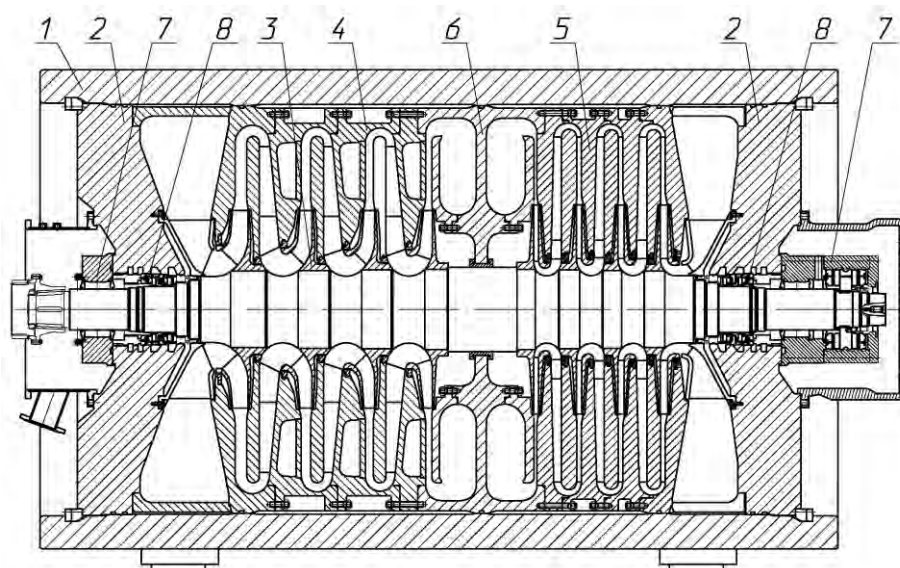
Відцентровий компресор С325ГЦ2-650/6-56М12 потужністю 25 МВт агрегату ГПА-Ц-25СД/0,58-5,5М1:1 – корпус; 2 – кришки корпуса; 3 – ротор; 4 – ПЧ першої секції; 5 – ПЧ другої секції стиснення; 6 – збірна камера; 7 – мастильні підшипники; 8 – торцеві газодинамічні ущільнення ротора
